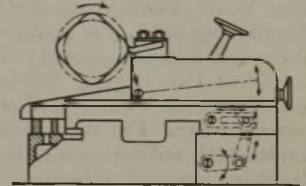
Schnitt einer Blockdrehbank mit schwingendem Support.
